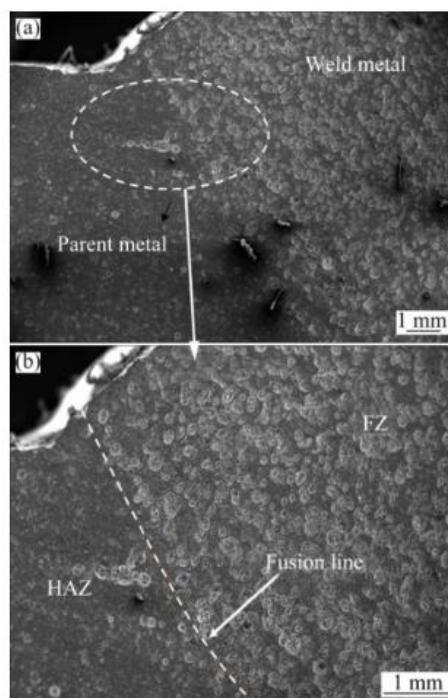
Liga de alumínio AA 6082 soldada por MIG em diferentes ampliações [37].
